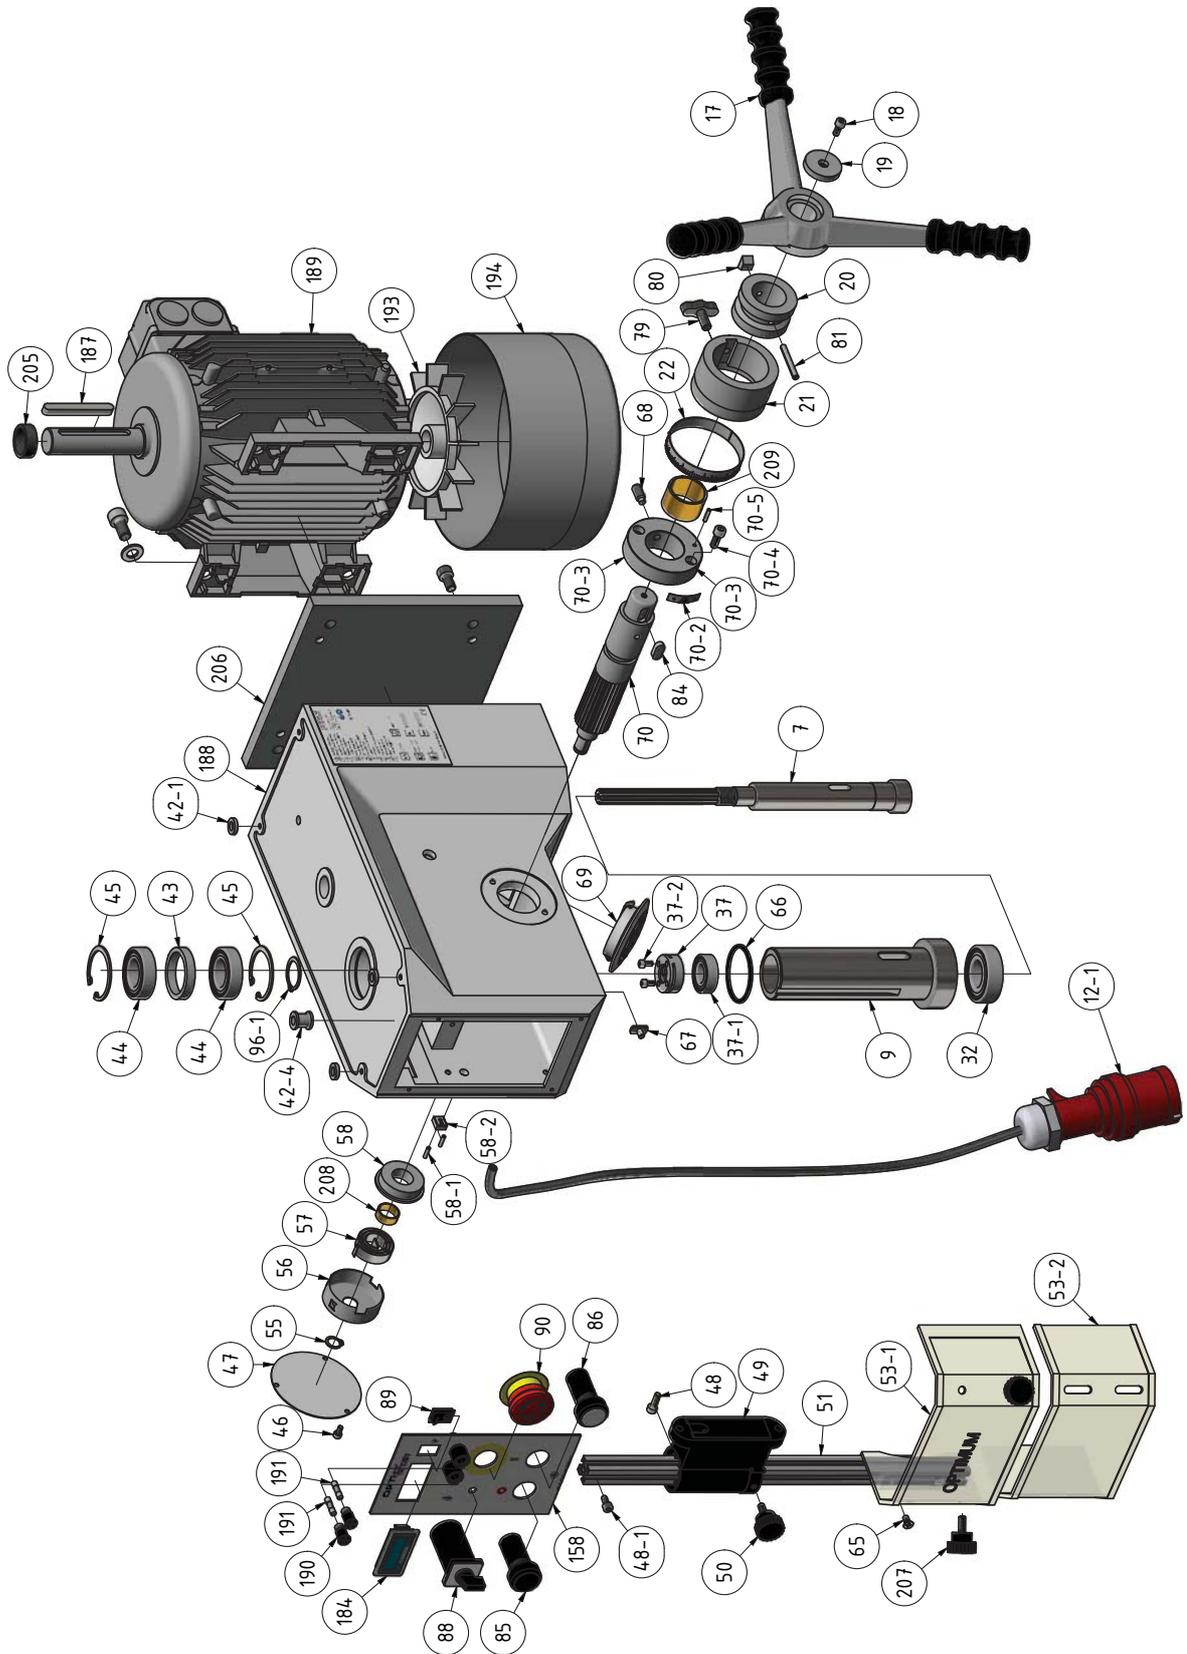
Bohrkopf DH24BV - Drilling head DH24BV
